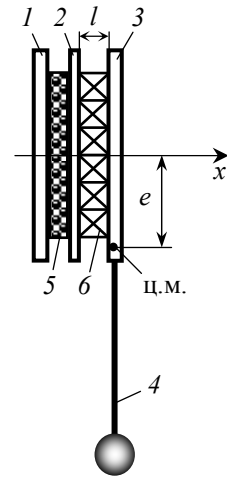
Схема конструкции гасителя колебаний маятникового типа
